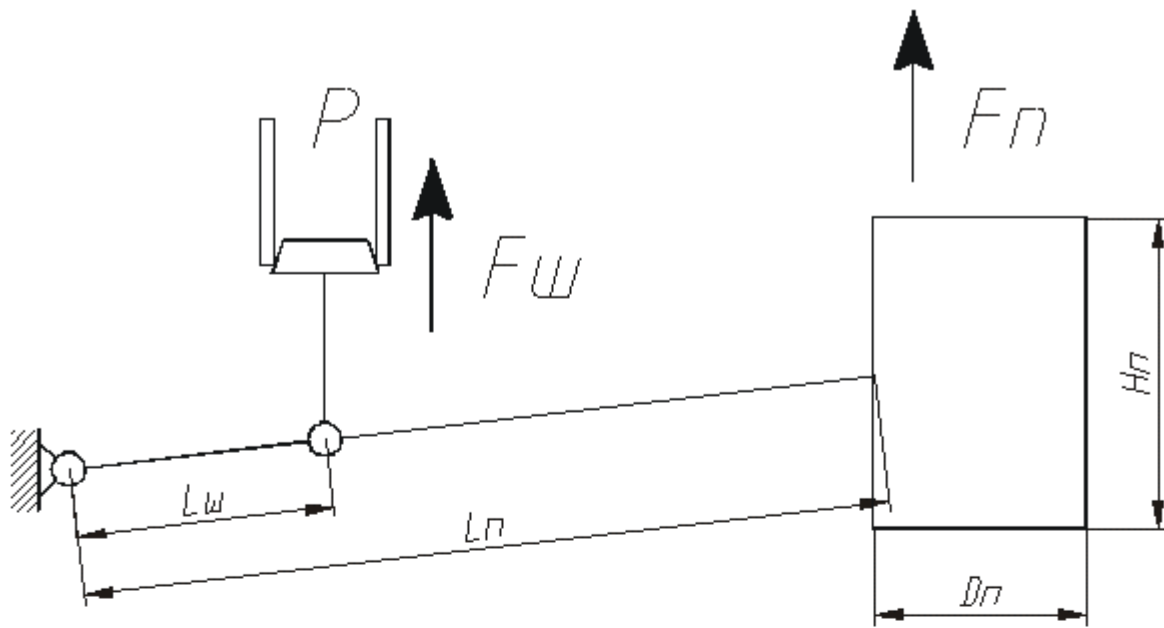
Розрахункова схема поплавкового пристрою.
